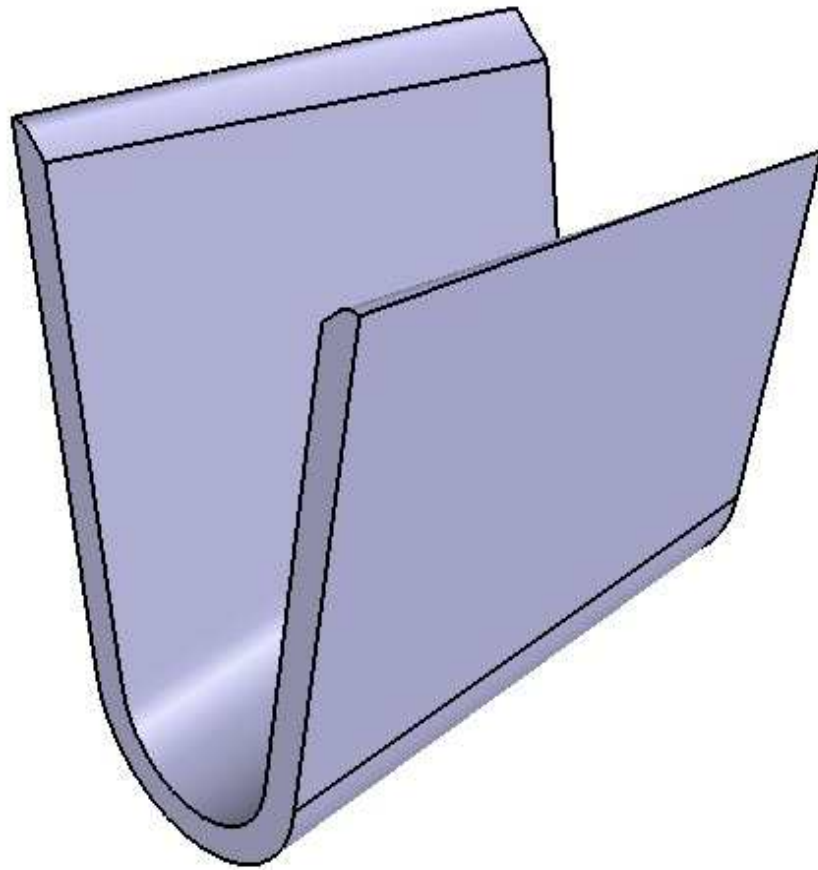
Vue isométrique de la tôle (forme de lèvre cylindrique inclinée).
